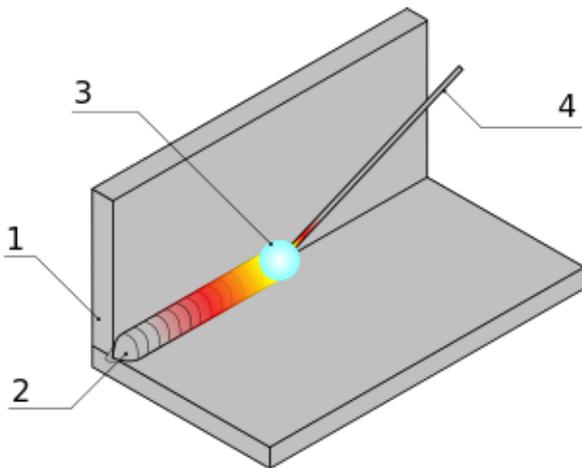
| Soldadura | Fuente: Wikipedia
